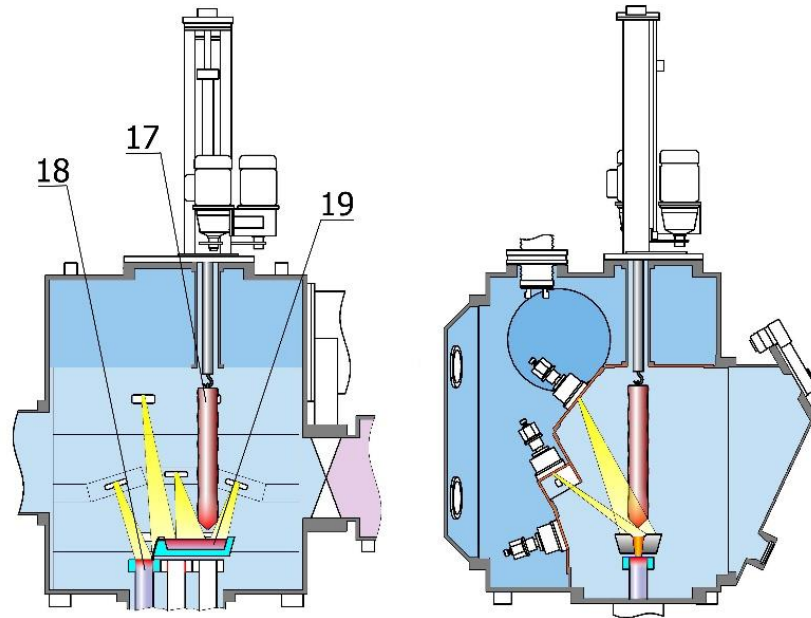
Схема переплаву заготовки в тигель через проміжну ємність: а - вид спереду; б - вид збоку
